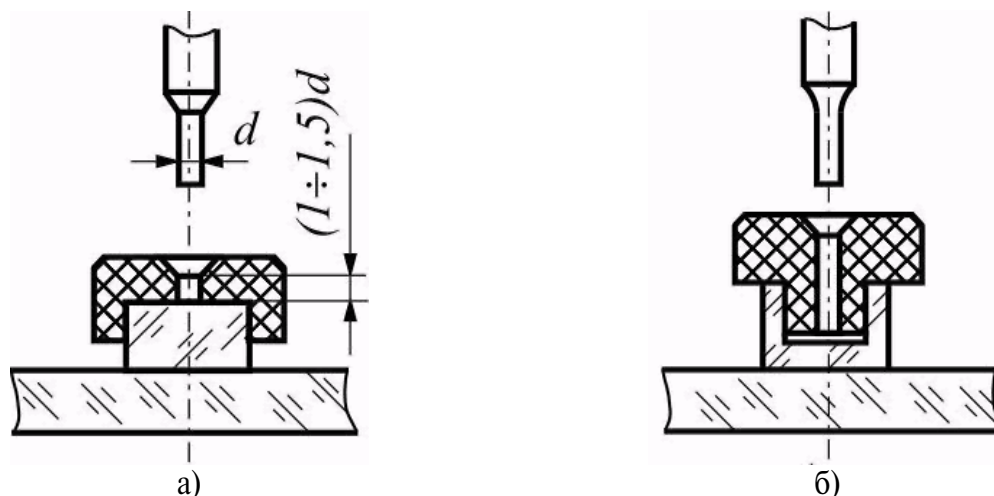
Схемы ультразвуковой обработки отверстий по кондуктору:
